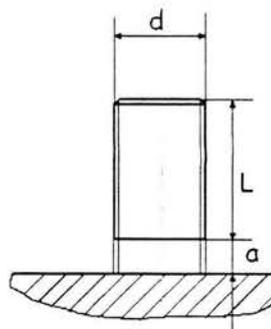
dimensiones para la Terminal de batería. Tipo alternativo
